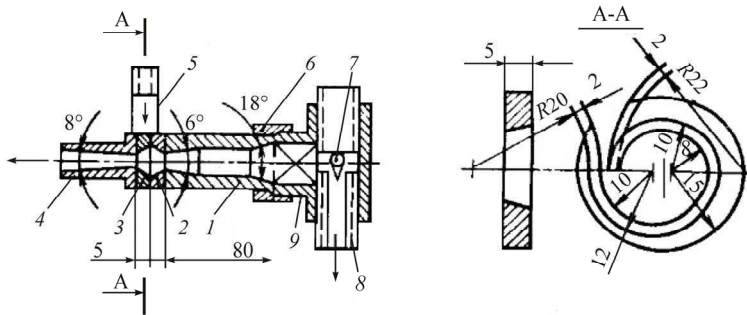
Вихревая трубка Парулейкара: 1 – камера разделения; 2 – конфузор; 3 – сопло; 4 – диффузор; 5 – патрубок ввода сжатого воздуха, 6 – соединительная гайка; 7 – игольчатый вентиль; 8 – патрубок вывода потока; 9 – развихритель
